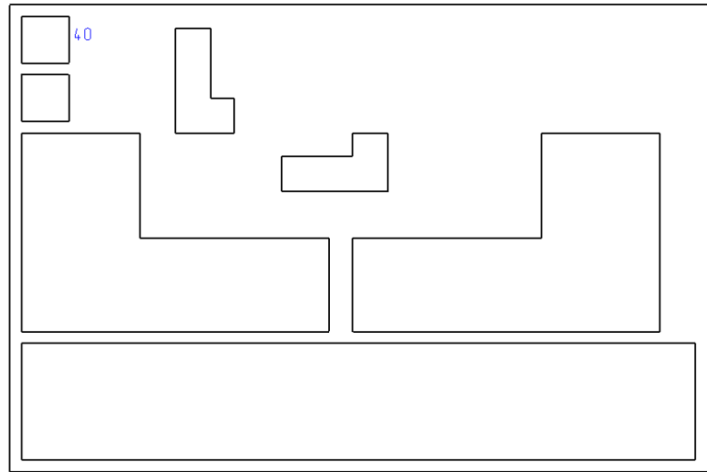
Plan de croire utilizat pentru exemplificarea metodei propuse
